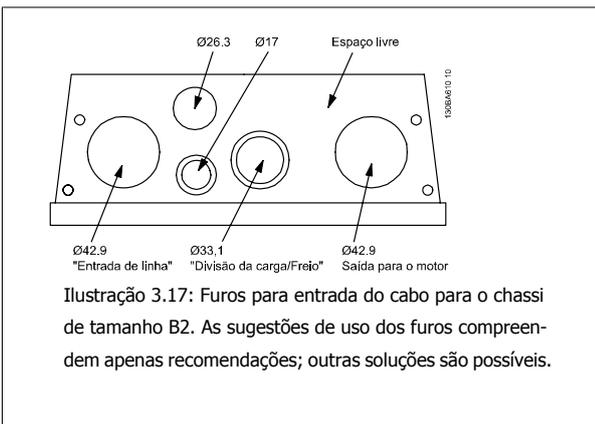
Furos para entrada do cabo para o chassis de tamanho B2. As sugestões de uso dos furos compreendem apenas recomendações; outras soluções são possíveis.
